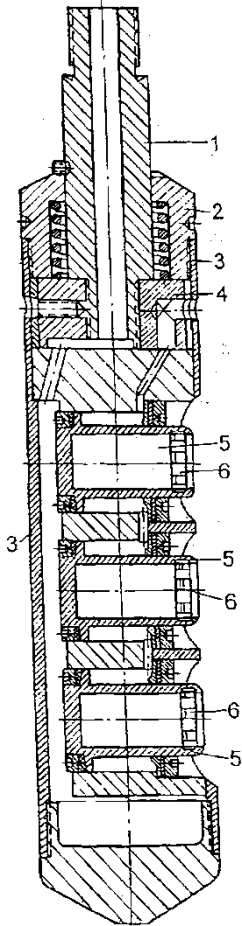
Боковой керноотборник гидравлического действия конструкции Ф.А.Шамшева и И.Калужного :
